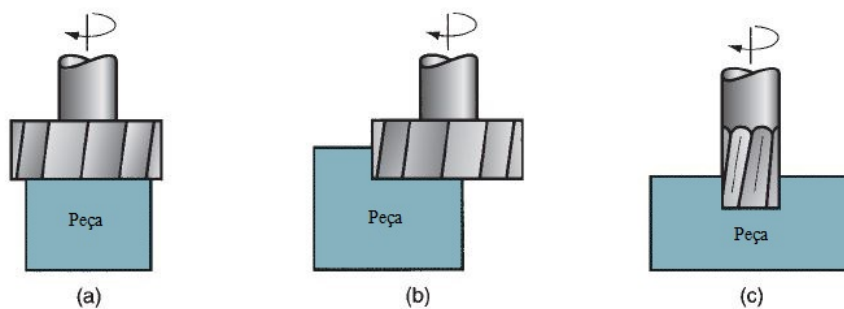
Fresagem Frontal: (a)fresagem frontal convencional; (b)fresagem frontal parcial; (c)fresagem de topo (Adaptado de [4]).
